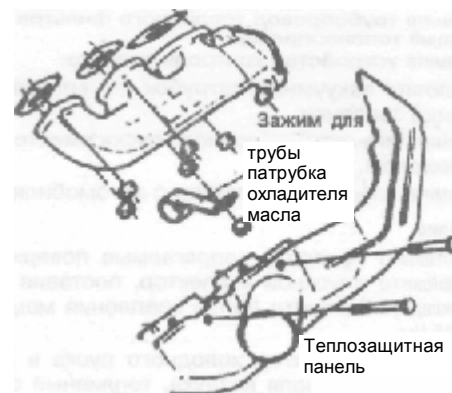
Выпускной коллектор в сборе — Двигатель B280F
